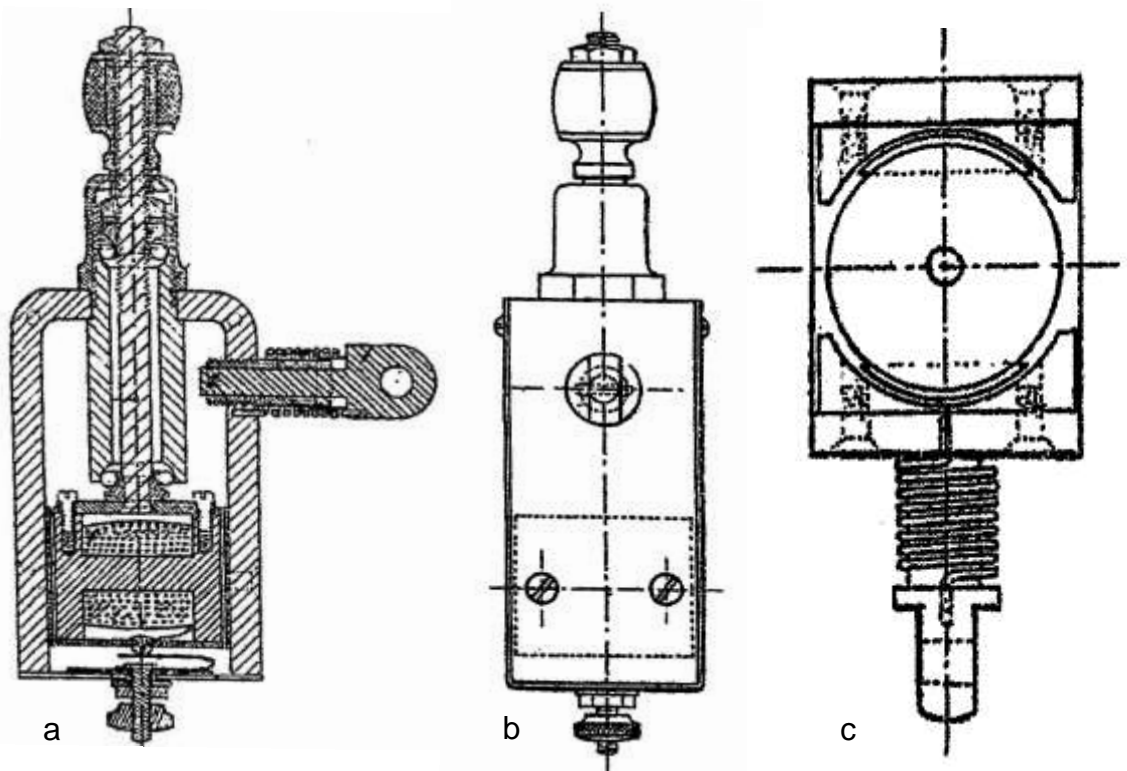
Zeichnungen im Patent N° 553.563: a) Längsschnitt, b) Seitenansicht mit Kippvorrichtung, c) Querschnitt durch die Polmitte
